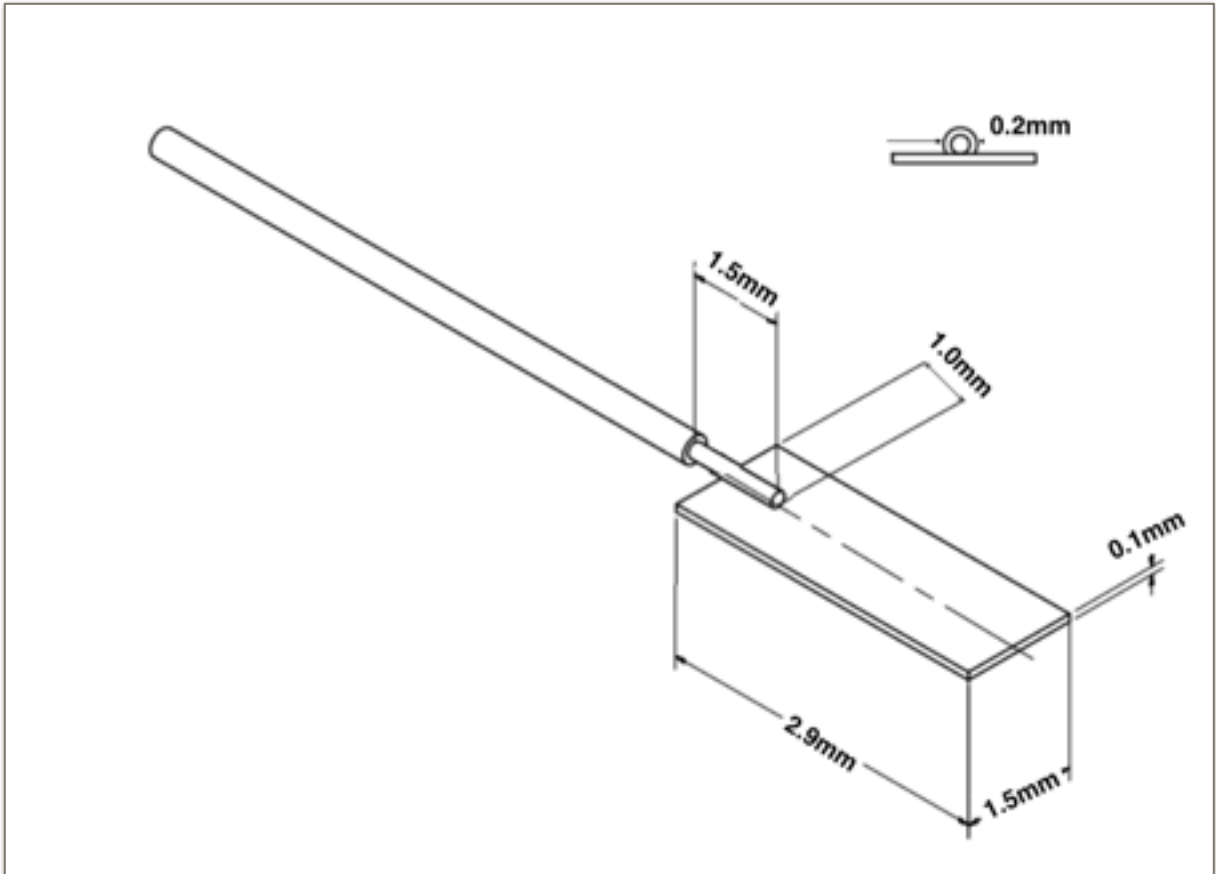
Dimensões do eletrodo. Dimensões da placa retangular (contato de Pt-Ir) do eletrodo e a relação de solda com o fio (região desencapada).
